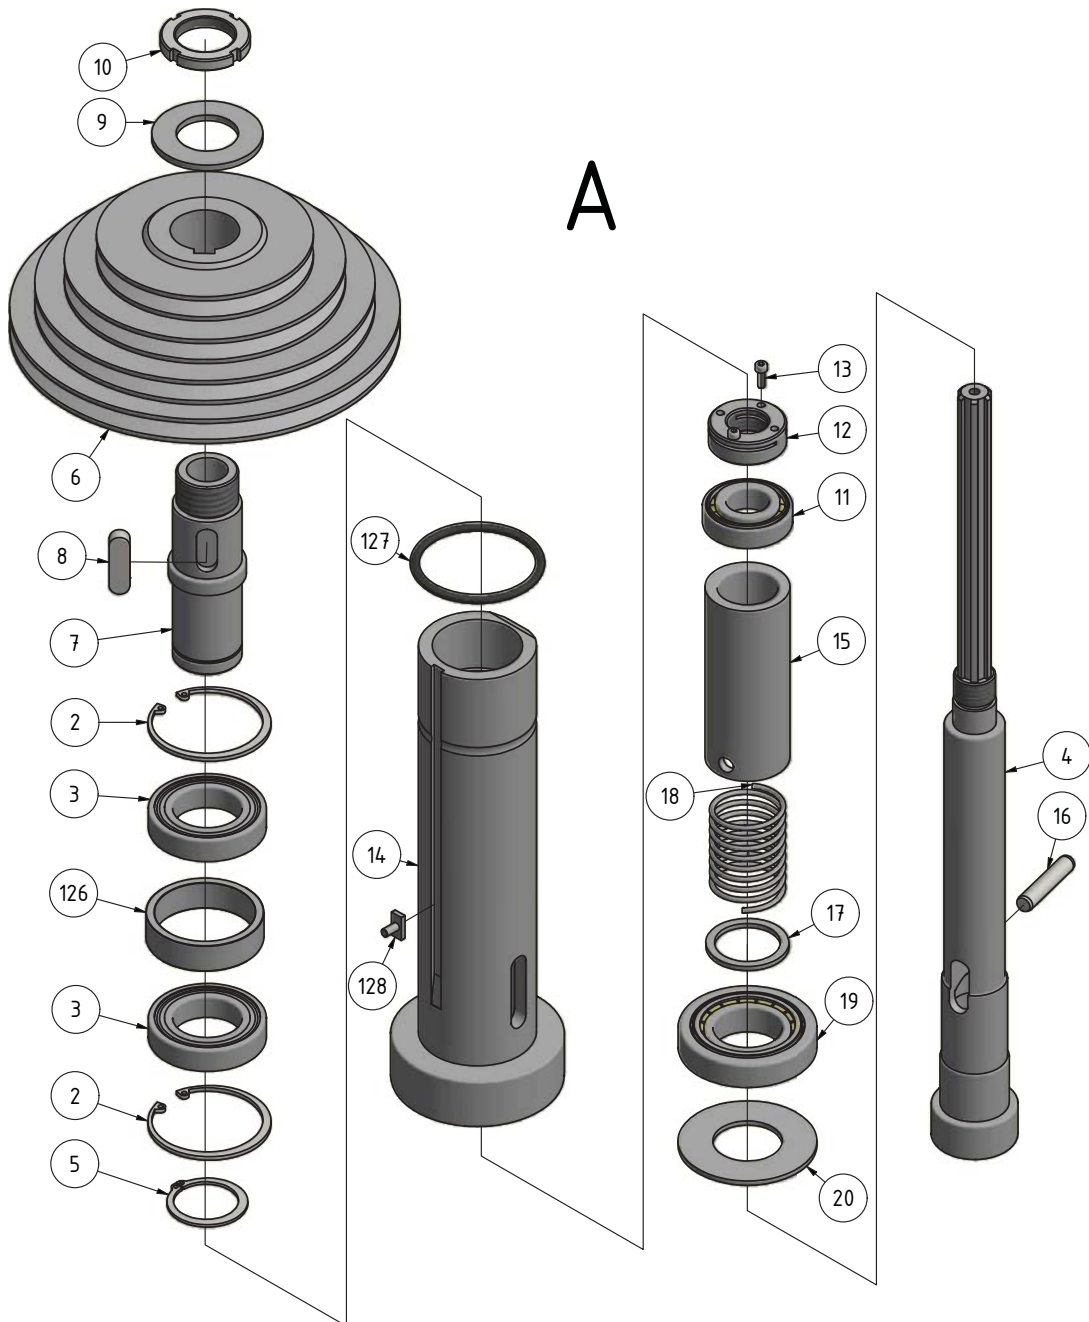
Bohrkopf 1 von 5 - Drilling head 1 of 5
